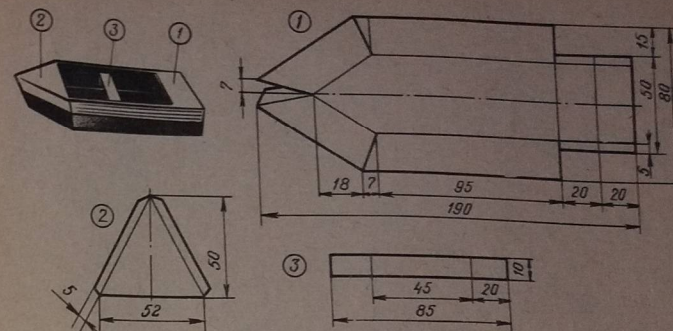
Модель лодки-плоскодонки: 1—корпус лодки; 2—носовая часть; 3—банка
